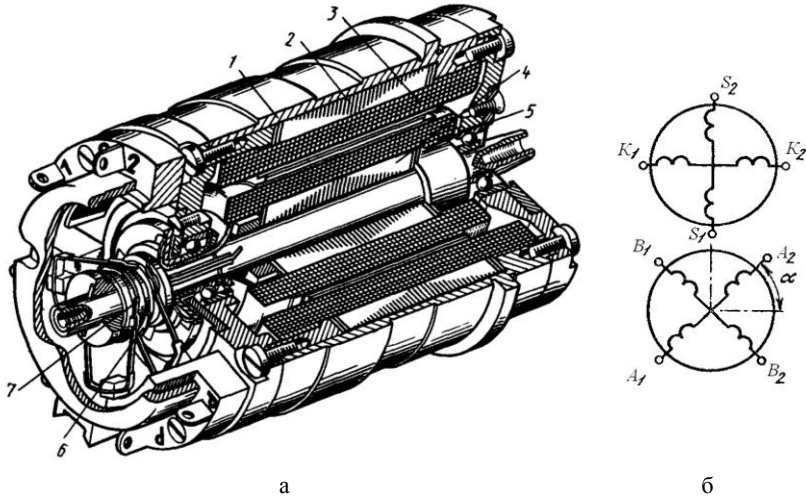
Устройство вращающегося трансформатора: 1 – корпус; 2 – статор; 3 – обмотка статора; 4 – ротор; 5 – обмотка ротора; 6 – контактные кольца; 7 – щетки
